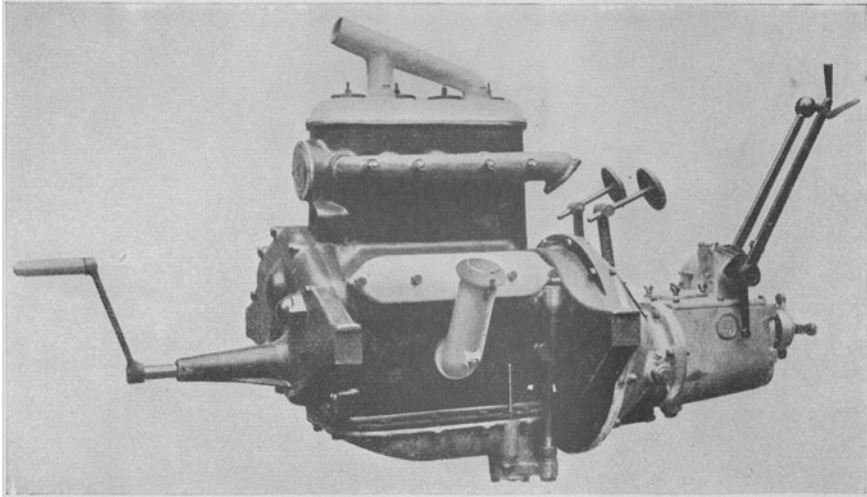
Vierzylinder-Kraftwagenmaschine mit Einschiebersteuerung.
